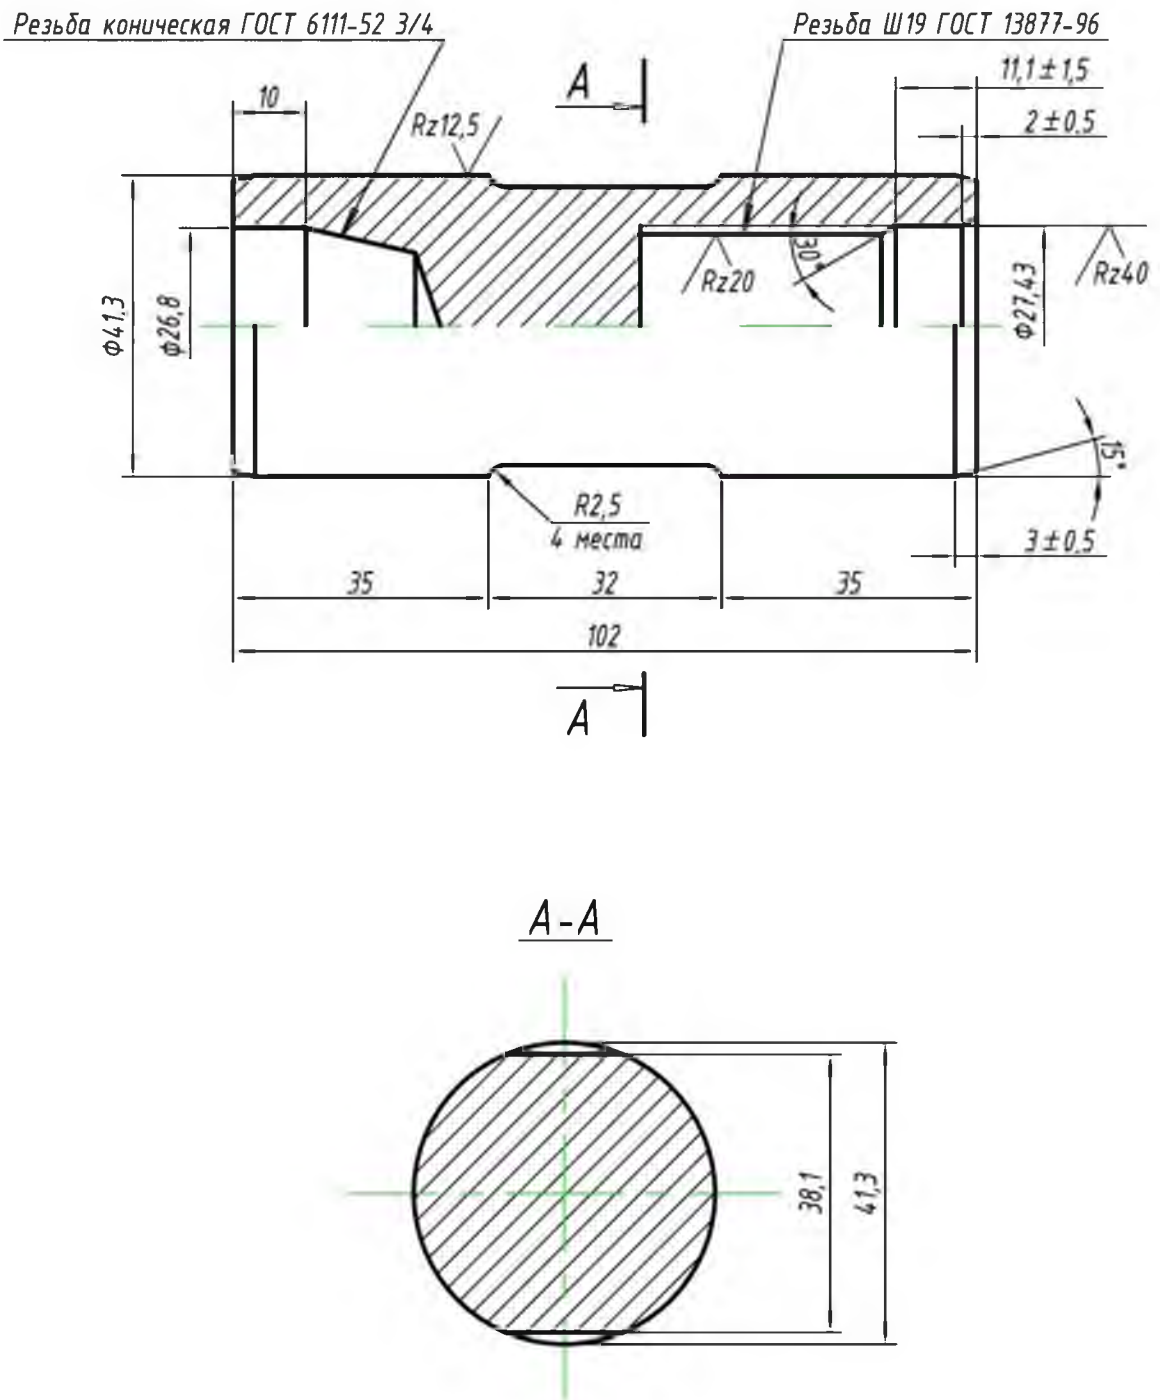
в - Соединительная головка с внутренней резьбой Ш19
